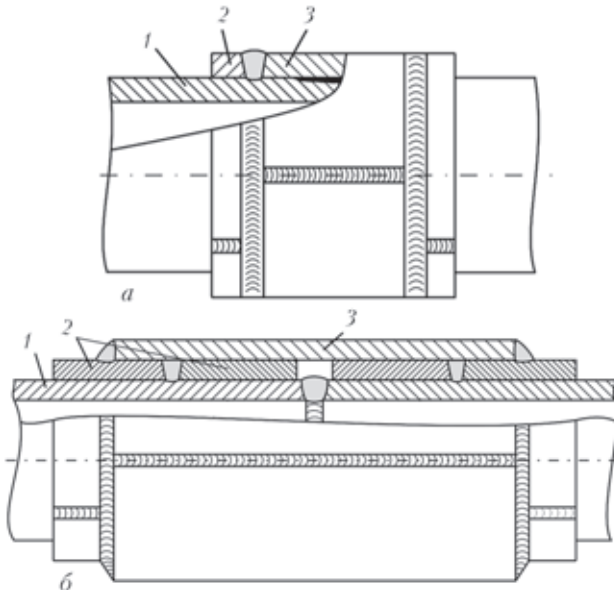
Конструктивно-технологические схемы ремонта МТ под давлением с использованием нахлесточно-стыковых сварных соединений: а — герметичная; б — двухслойная муфта; 1 — трубопровод; 2 — технологические кольца; 3 — муфта
